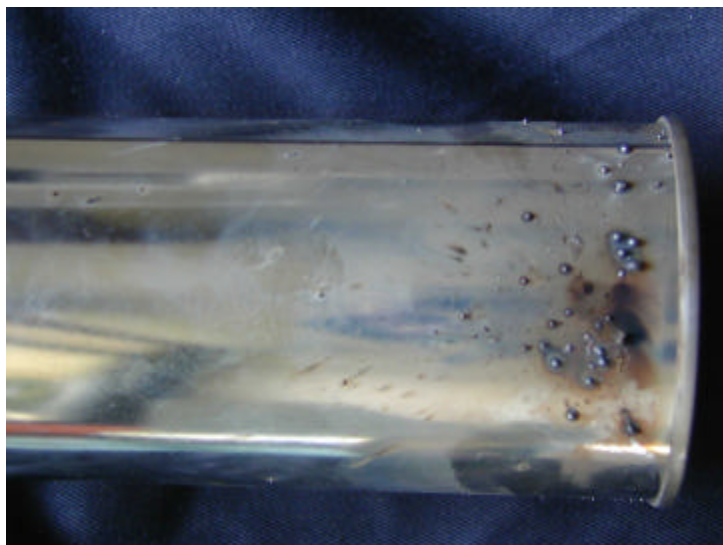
Anhaftende Schweißperlen beim Schutzgasschweißen
